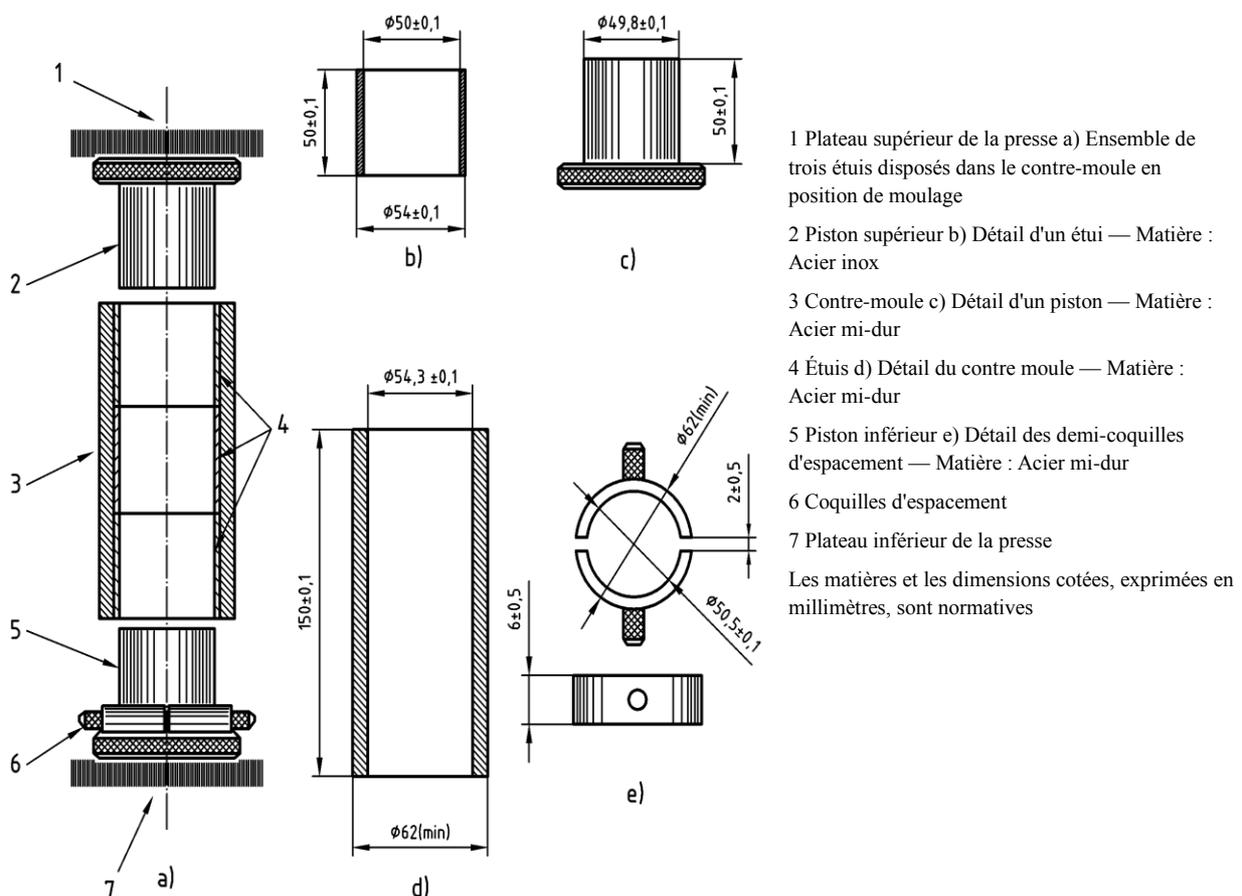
Ensemble de moulage utilisé pour la confection des éprouvettes
